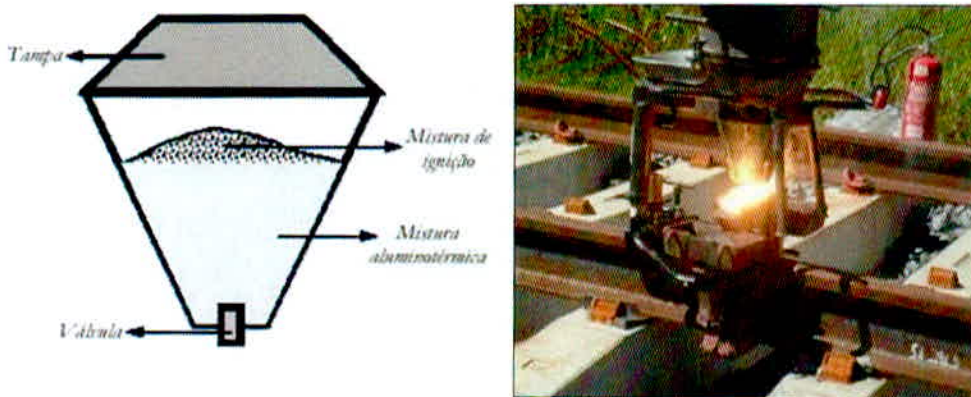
Cadinho utilizado no processo de soldagem aluminotérmica.
